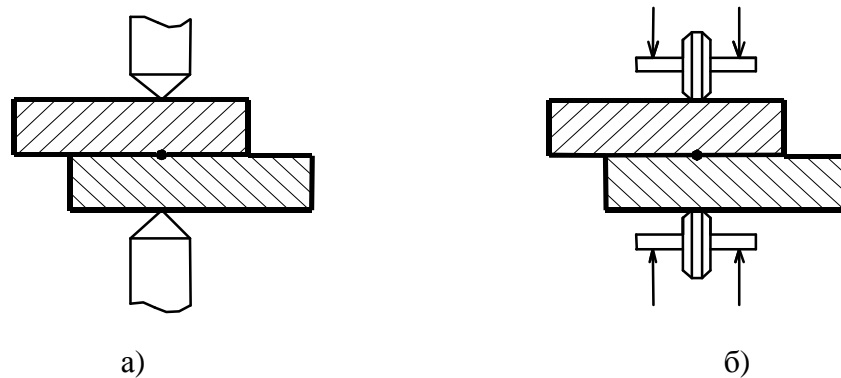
Контактне зварювання: а – точкове; б – шовне
